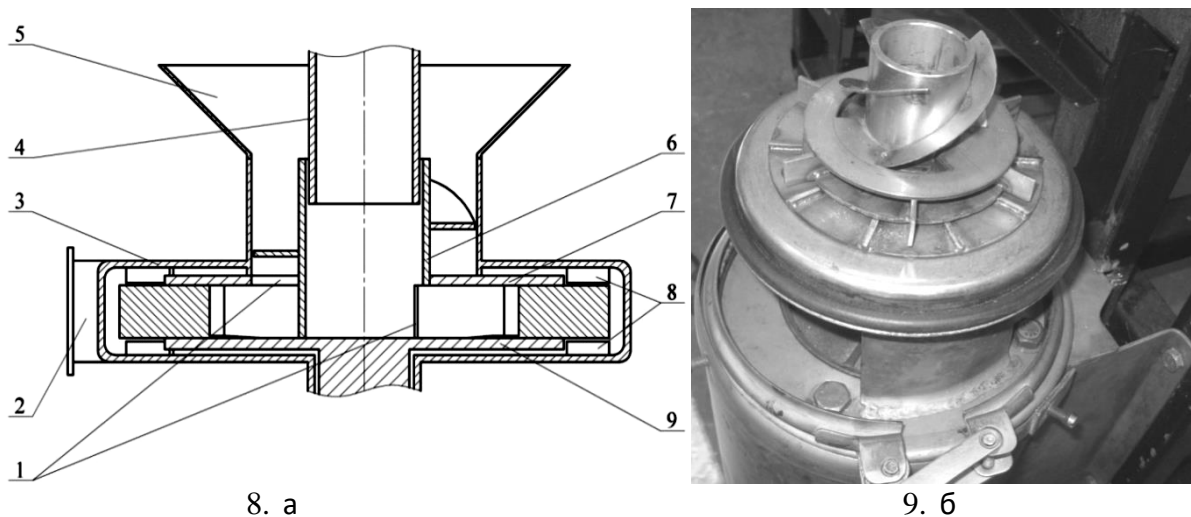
Схема (а) и общий вид (б) установки для приготовления жидких кормовых смесей
